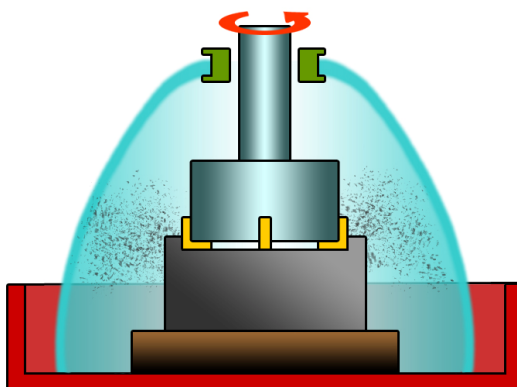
Princip upínání elektrod systému 3R Macro
